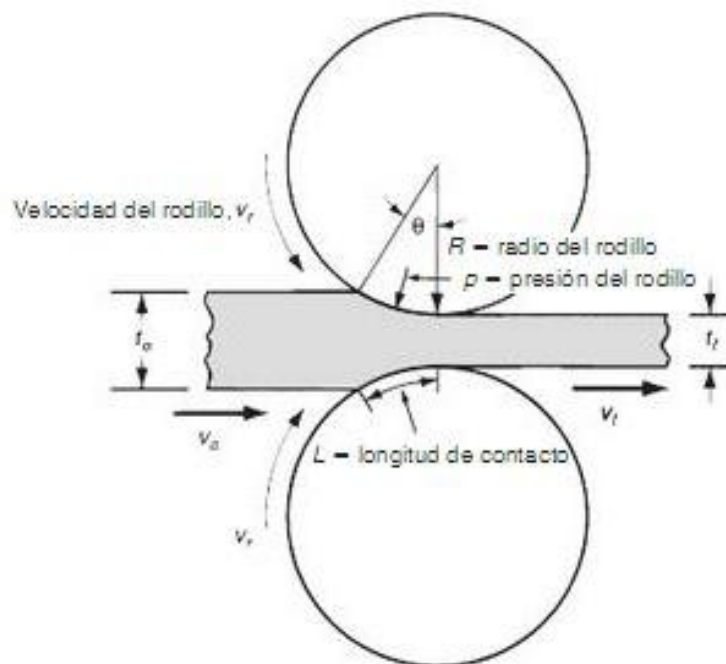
1 – Vista lateral del laminado plano [3].
